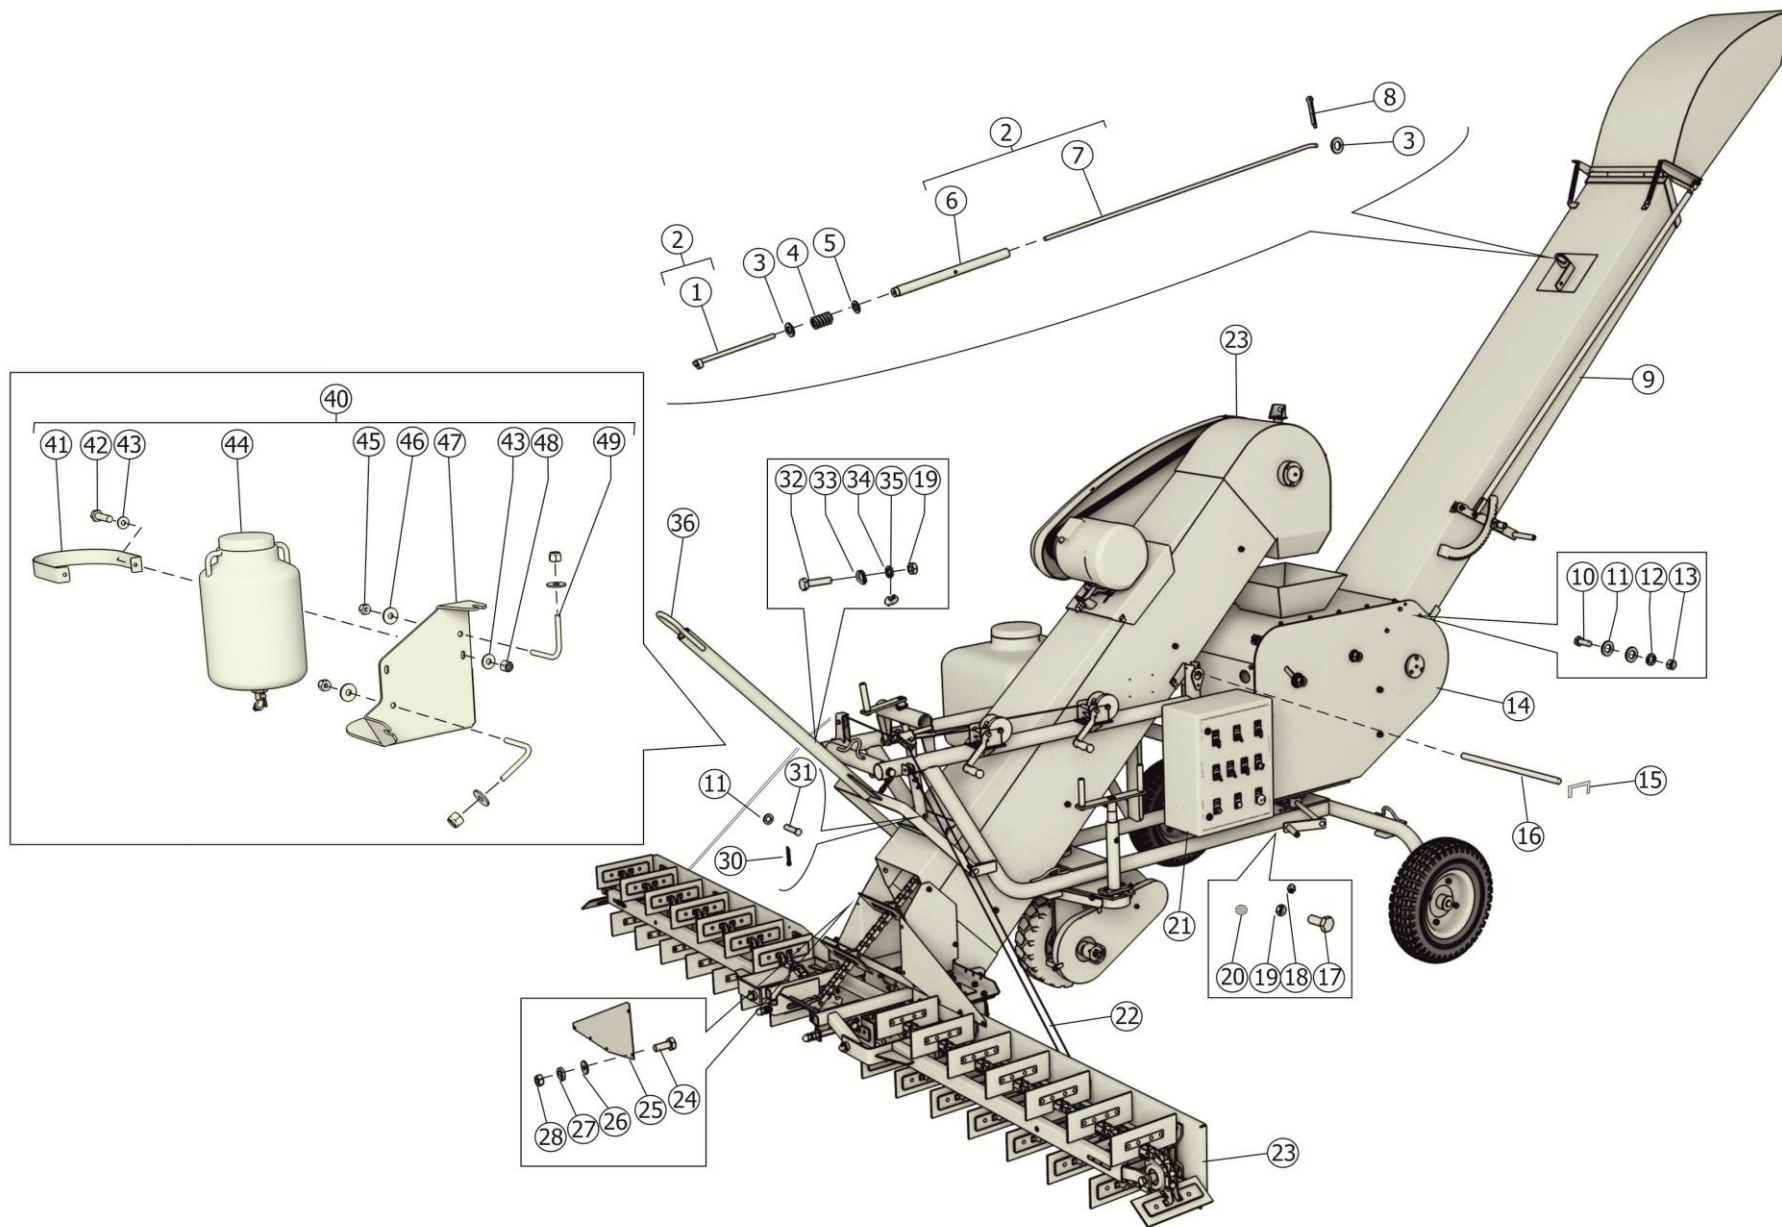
Комплекс зерноперерабатывающий ЗМП-ПСМ-01/-02. Общий вид
